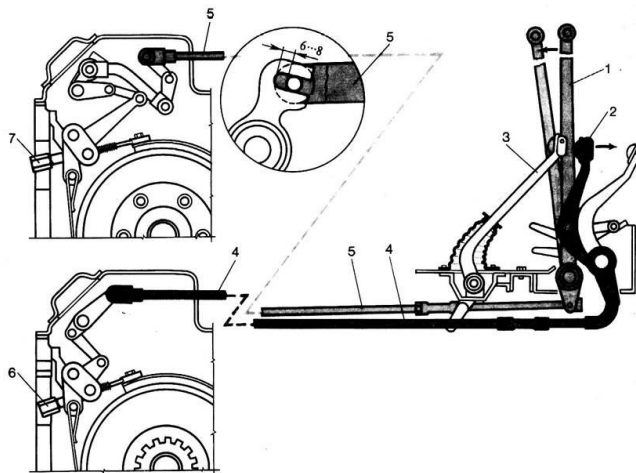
Механизм управления: 1 - рычаг управления тормозом солнечной шестерни; 2 - педаль управления остановочным тормозом; 3 - педаль управления сцеплением; 4 - тяга остановочного тормоза; 5 - тяга тормоза солнечной шестерни; 6 - регулировочная гайка остановочного тормоза; 7 - регулировочная гайка тормоза солнечной шестерни
